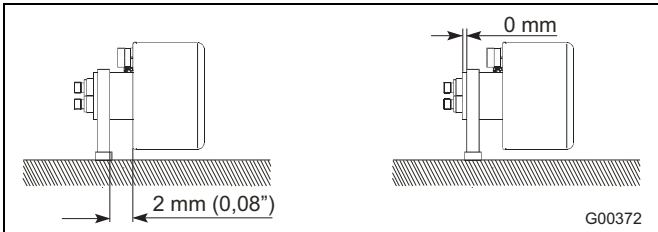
Einbau DN 1,5 (1/16“) – horizontal
